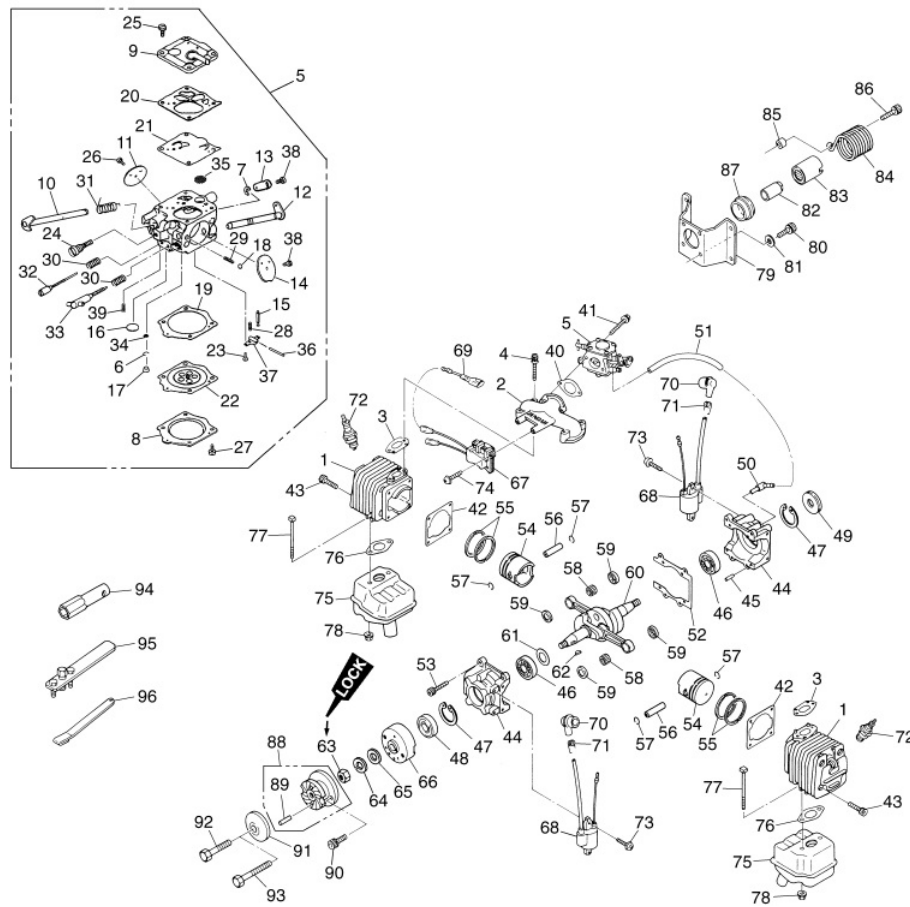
Explosionado del motor Zenoah GT80 (Fuente: Zenoah Inc.)
